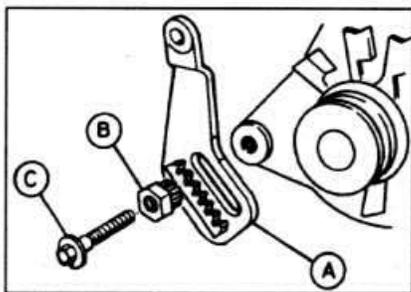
Регулировка натяжения приводного клинового ремня с реечной передачей.
